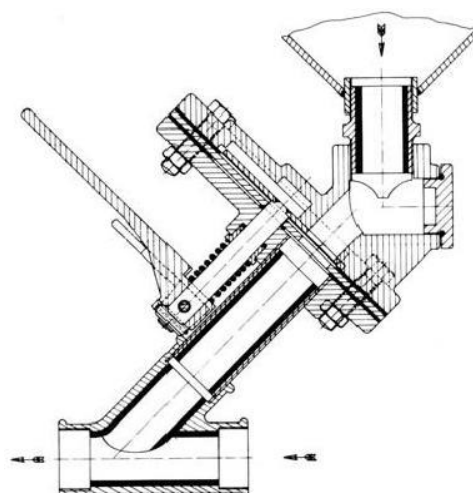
Дозировочный клапан с эксцентрической системой потока абразива.
